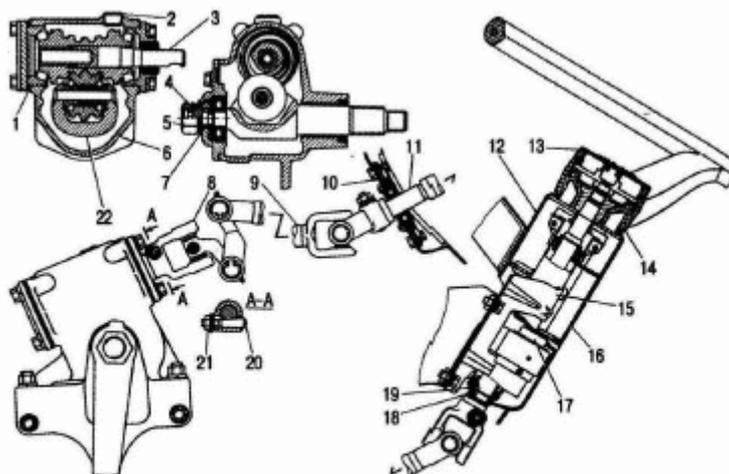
Рулевое управление: 1 – прокладка; 2 – пробка наливного отверстия; 3 – вал с червяком; 4 – регулировочный винт; 5 – гайка; 6 – картер; 7 – стопорная шайба; 8 – вилка; 9 – нижний карданный вал; 10 – подшипник с уплотнителем; 11 – средний карданный вал; 12 – верхний кожух; 13 – накладка; 14 – рулевое колесо; 15 – колонка; 16 – нижний кожух; 17 – замок руля; 18 – регулировочная гайка; 19 – шайба; 20 – клин; 21 – самостопорящаяся гайка; 22 – вал сошки с трехребровым роликом
